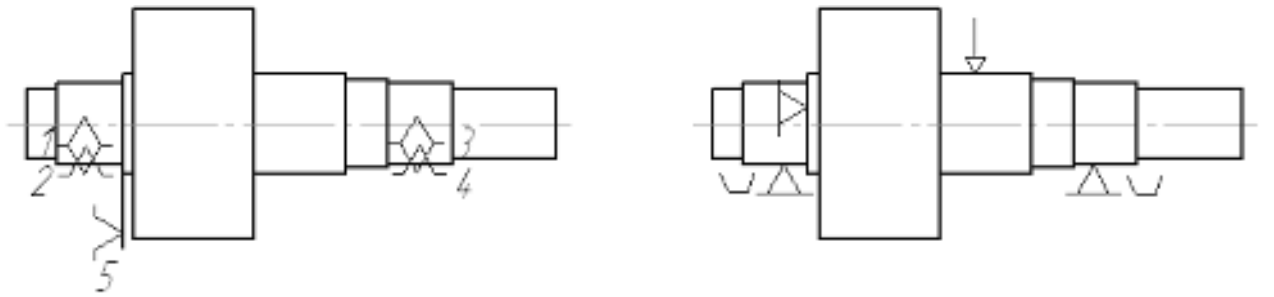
Схема базування і закріплення деталі на фрезерно-центрувальній операції
